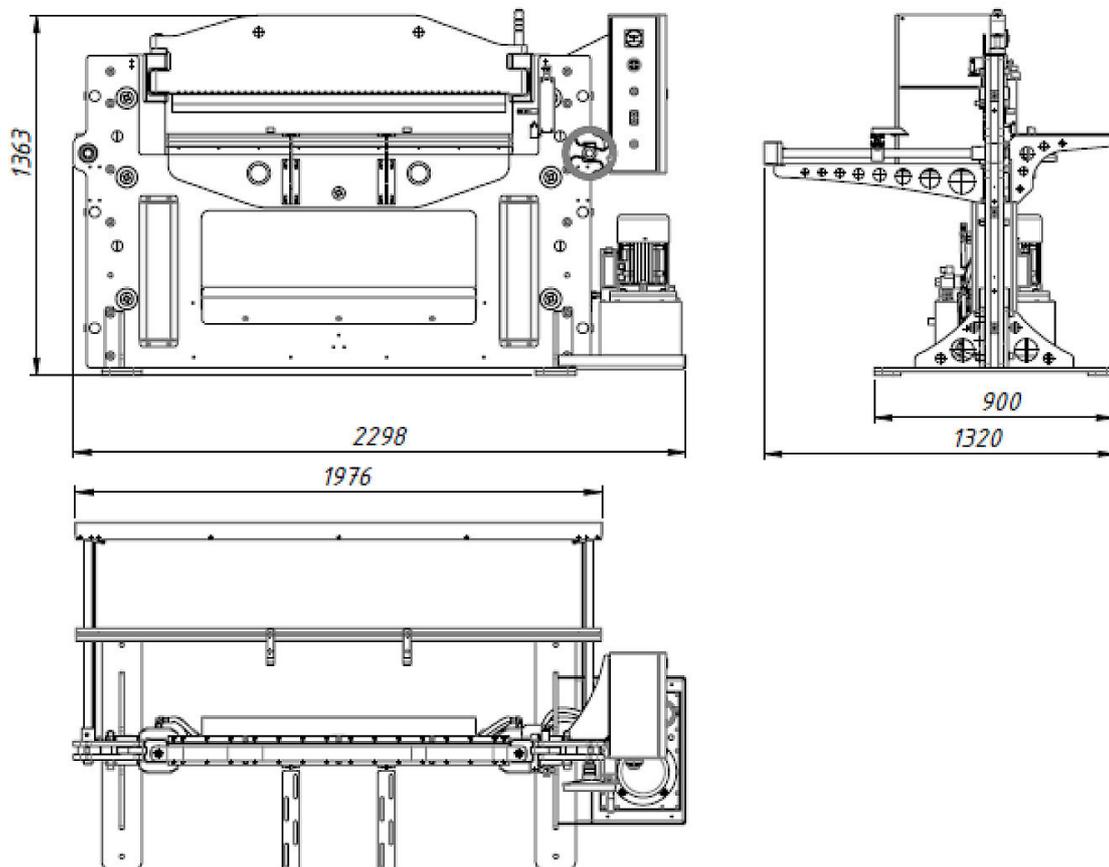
Grundriss der Werkstatt-Abkantpresse
